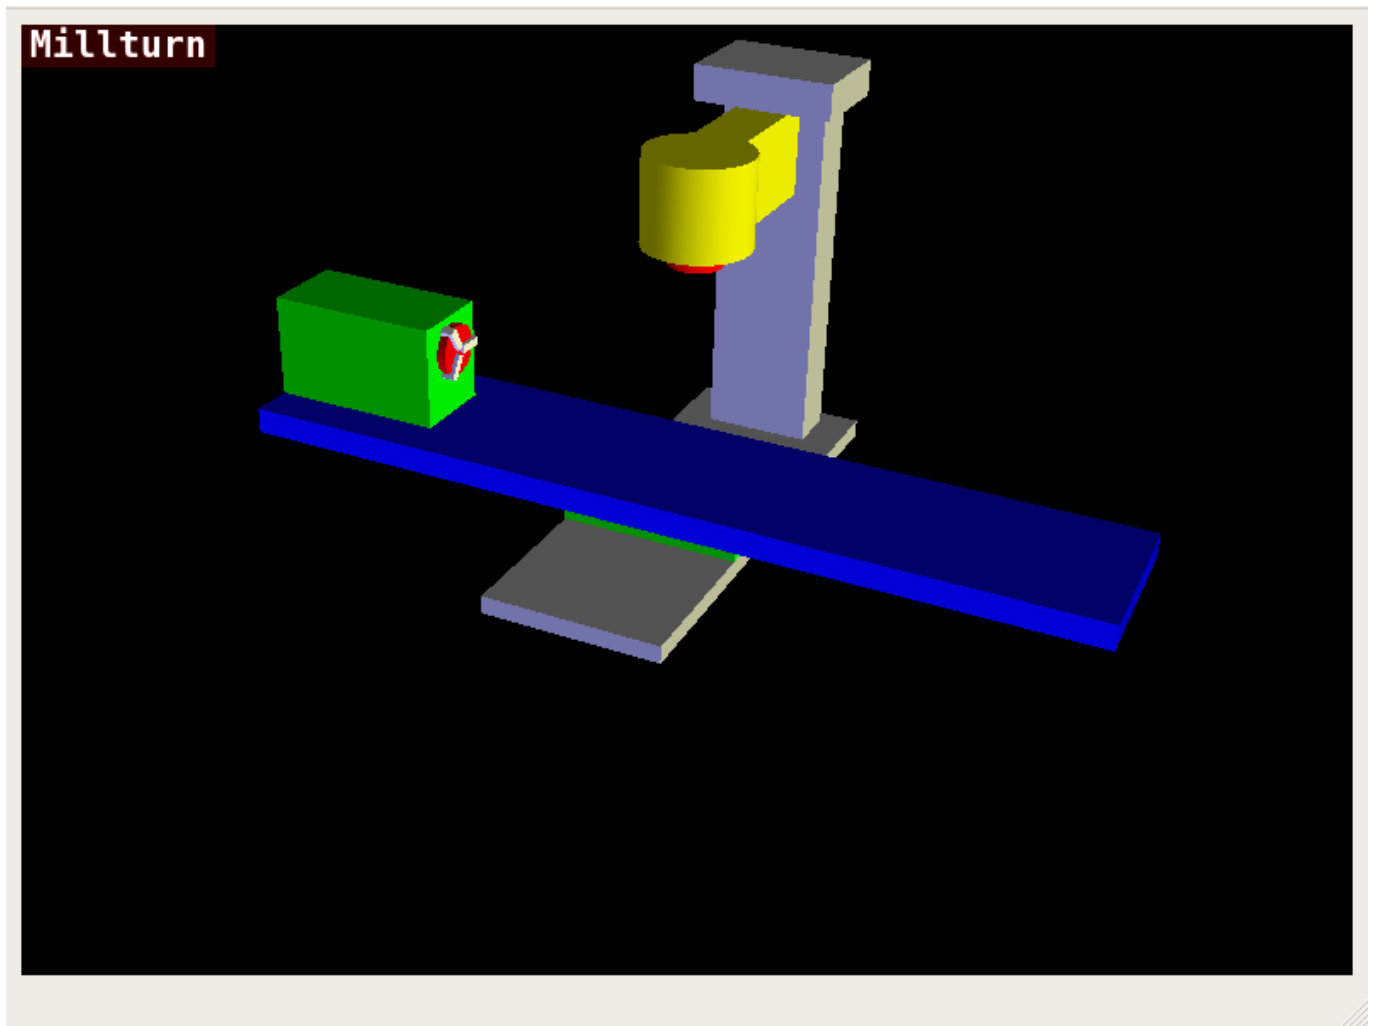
QtVCP vismach\_millturn - 4 Axis MillTurn 3D View Panel
